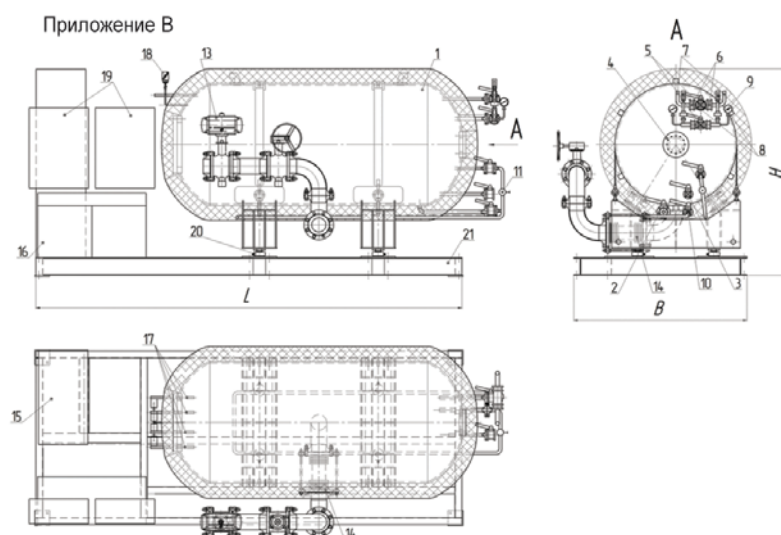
резервуар цилиндрический горизонтальный; 2 – патрубок заправочный жидкой фазы; 3 – патрубок заправочный газовой фазы; 4 – уровень визуальный; 5 – кран трехходовой; 6 – мембрана предохранительная; 7 – отводящий патрубок сброса давления; 8 – предохранительный клапан; 8 – манометр показывающий; 10 – кран шаровый; 11 – регулятор давления; 12 – кран шаровый; 13 – пневмопривод реверсивный; 14 – компенсатор; 15 – шкаф управления пуском; 16 – холодильный агрегат; 17 – испаритель; 18 – регулятор давления; 19 – электрический шкаф управления; 20 – тензOMETрический датчик; 21 – рама монтажная
